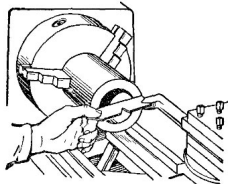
Установка резьбового резца по шаблону при нарезании внутренней резьбы
